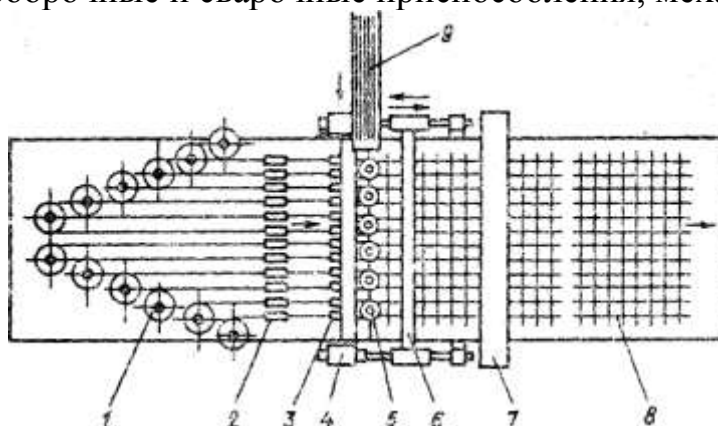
Схема автоматической машины для сварки арматурных сеток и каркасов
